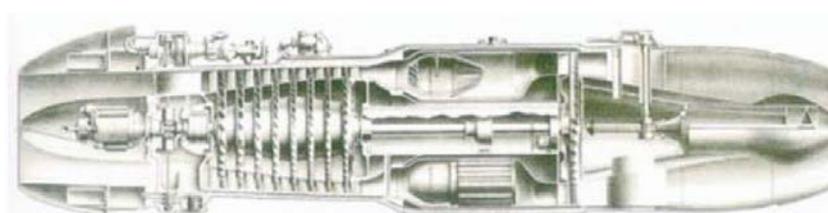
Первый реактивный двигатель боевого самолета с осевым компрессором (1940-е гг. Германия)
